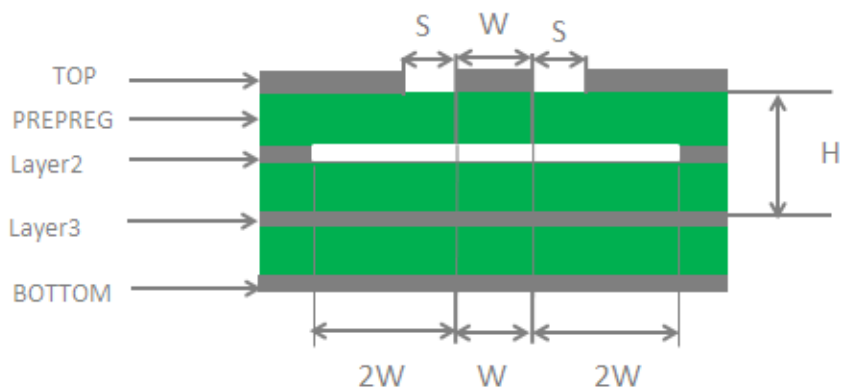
四层 PCB 板共面波导结构 (参考地为第三层)
